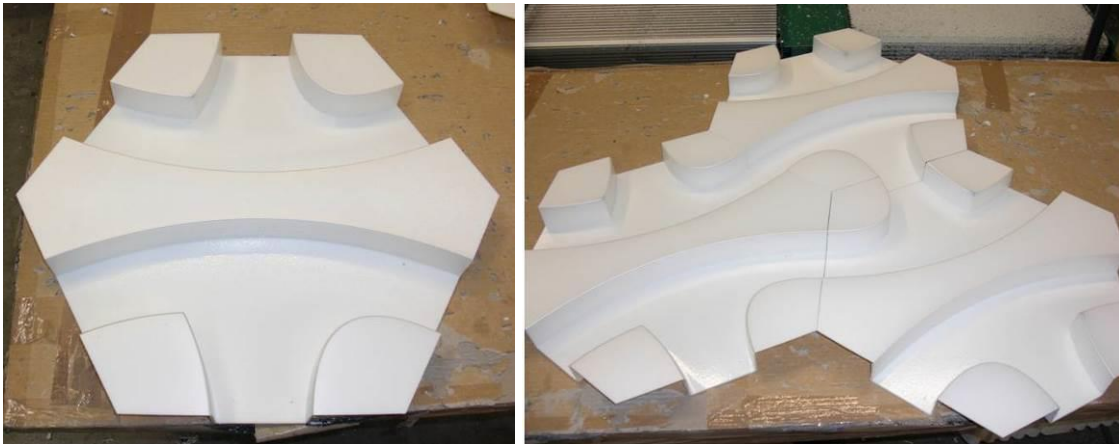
Formteile ohne Tiefziehrand ©BAUER THERMOFORMING
